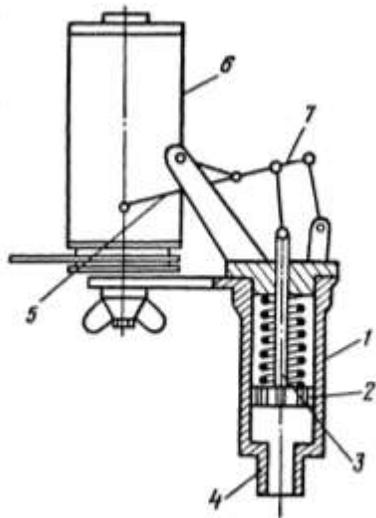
Схема индикатора: 1 — цилиндр; 2 — поршень; 3 — пружина; 4 — патрубок для соединения с насосом; 5 — гайка; 6 — барабан; 7 — рычаг
